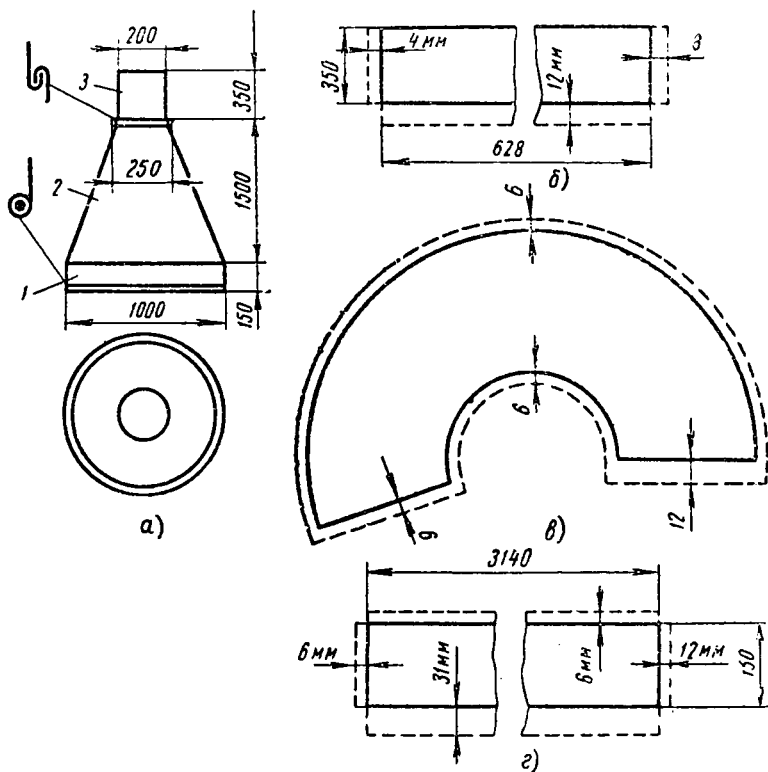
Вытяжной зонт с круглым основанием (а), развертка патрубка (б), развертка обечайки (в), развертка обода (г)
